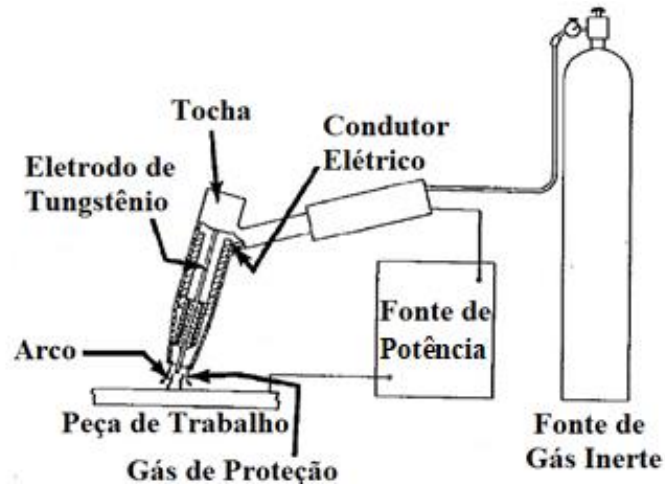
Componentes do equipamento de soldagem TIG [AWS, 2001].
